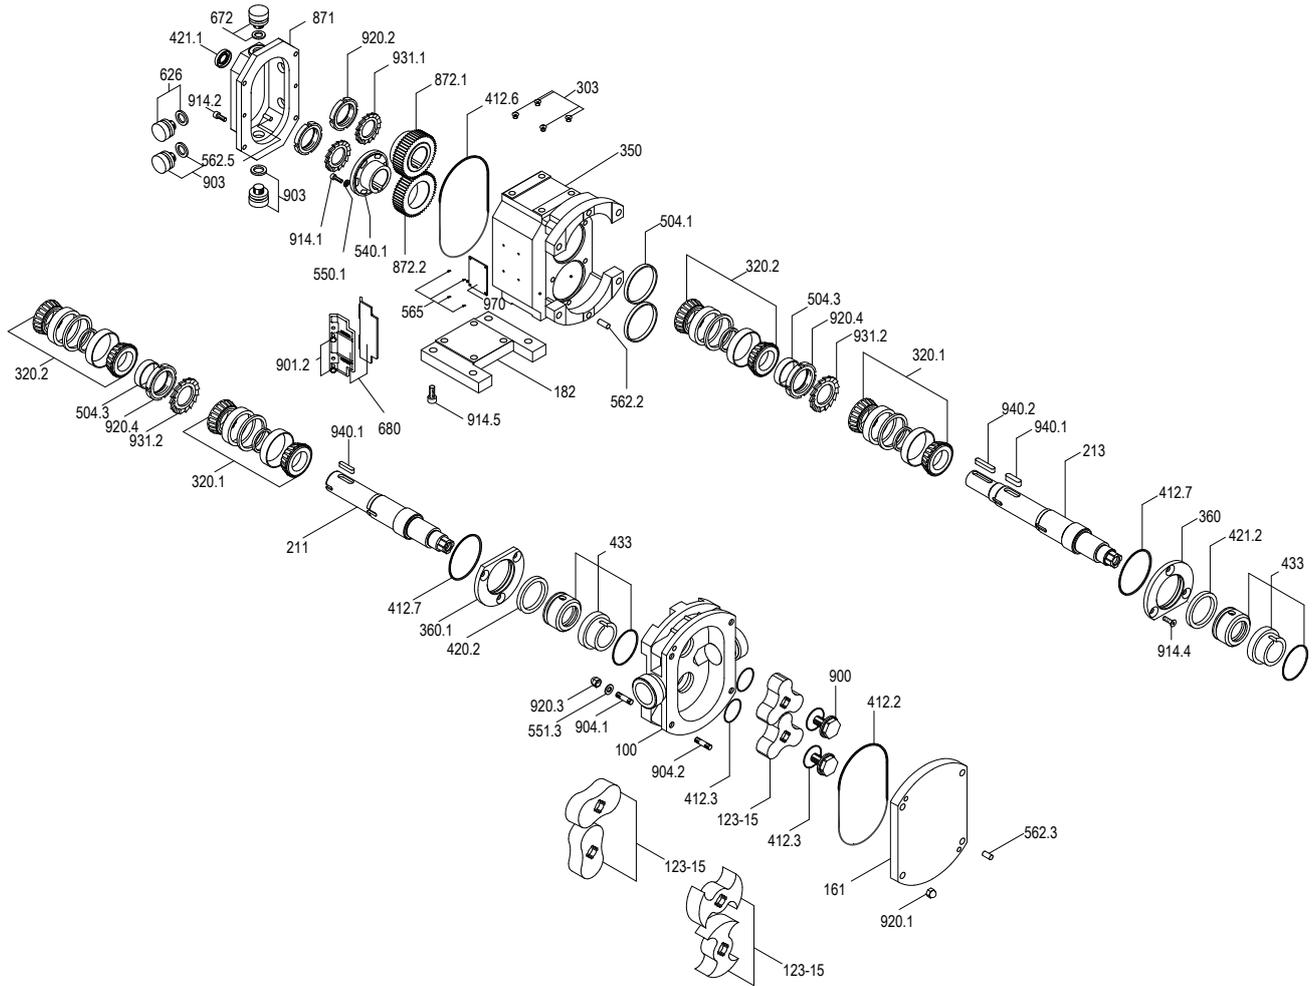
Explosionszeichnung Vitallobe Baugröße 550
